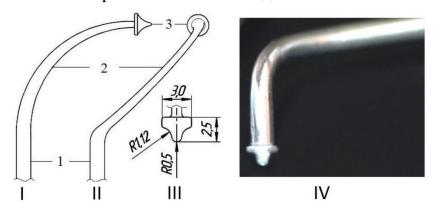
Схема и фотография разработанного нами штопфера: I - вид сбоку; II - вид сверху; III - параметры рабочей поверхности инструмента; IV — внешний вид штопфера. 1 - ручка инструмента; 2 - изгиб рабочей части; 3 - рабочая поверхность.
